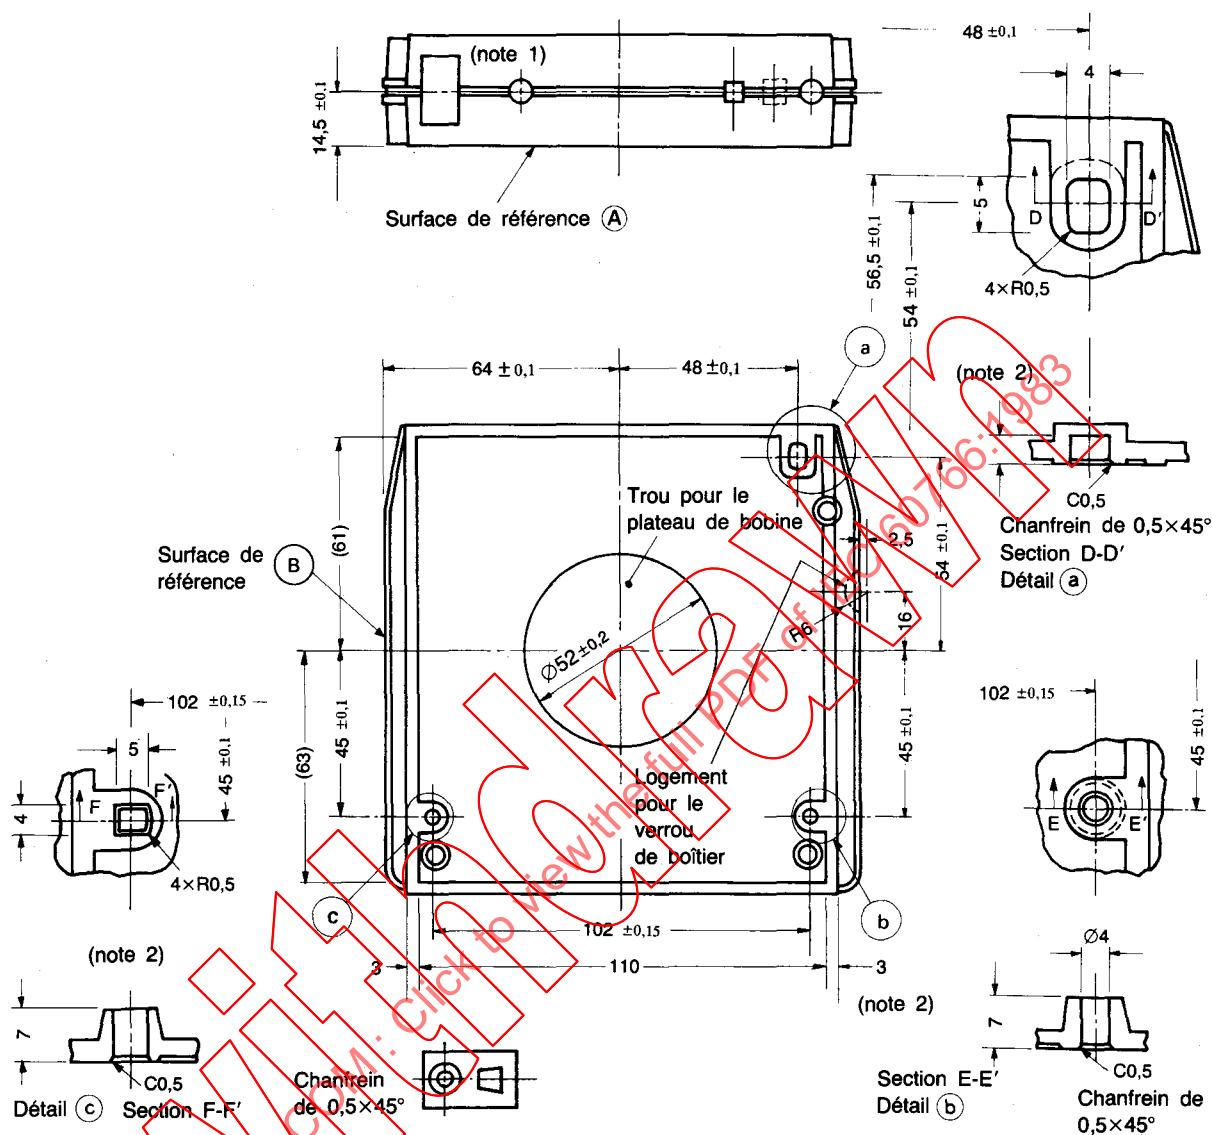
Vue inférieure et vue latérale du boîtier.
